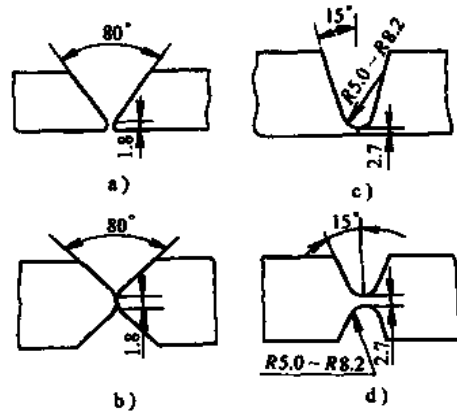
焊条电弧焊、TIG 焊镍基合金典型坡口形式
